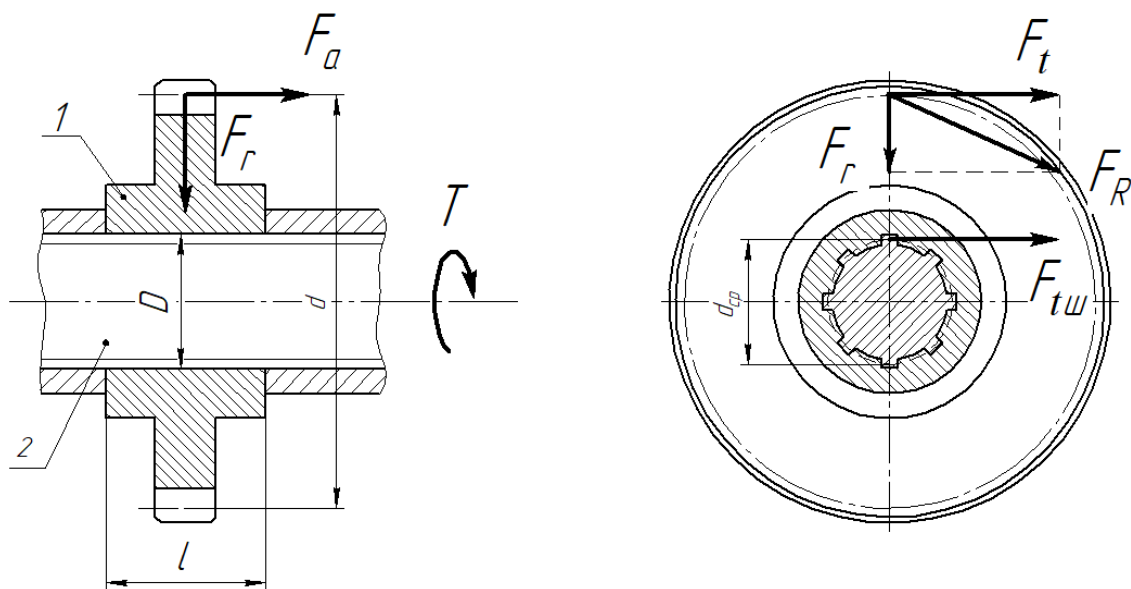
Соединение зубчатого колеса со шлицевым валом:
